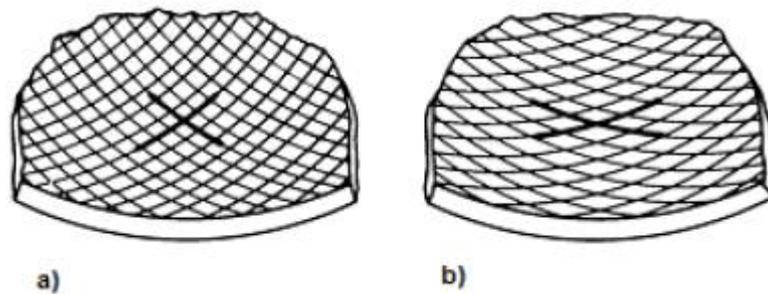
Diferentes ângulos de cruzamento – a) menor que 90° b) maior que 90°
